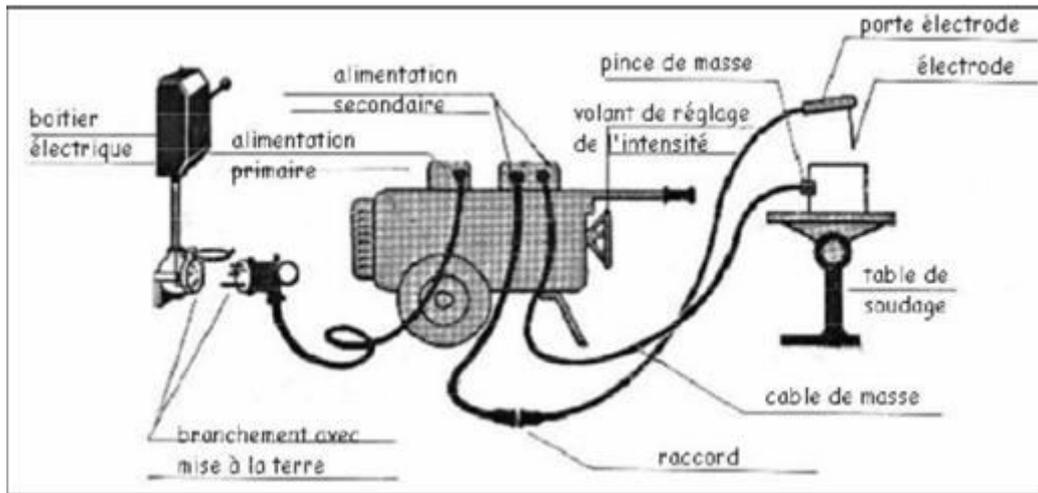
Principe de soudage à l'arc avec électrode enrobée.
